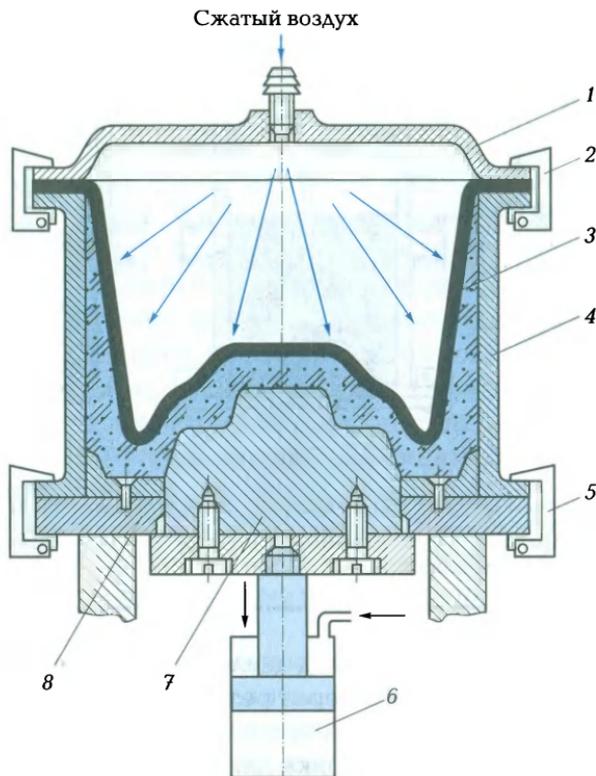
Установка для прессования оболочковых полуформ с протяжкой модели через резиновую диафрагму:
